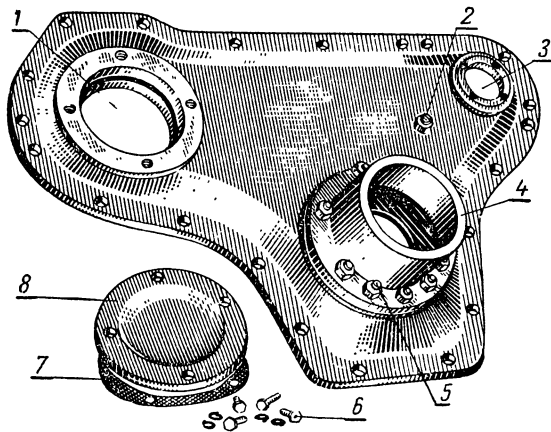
Крышка картера шестерен дизеля Д-54А:
